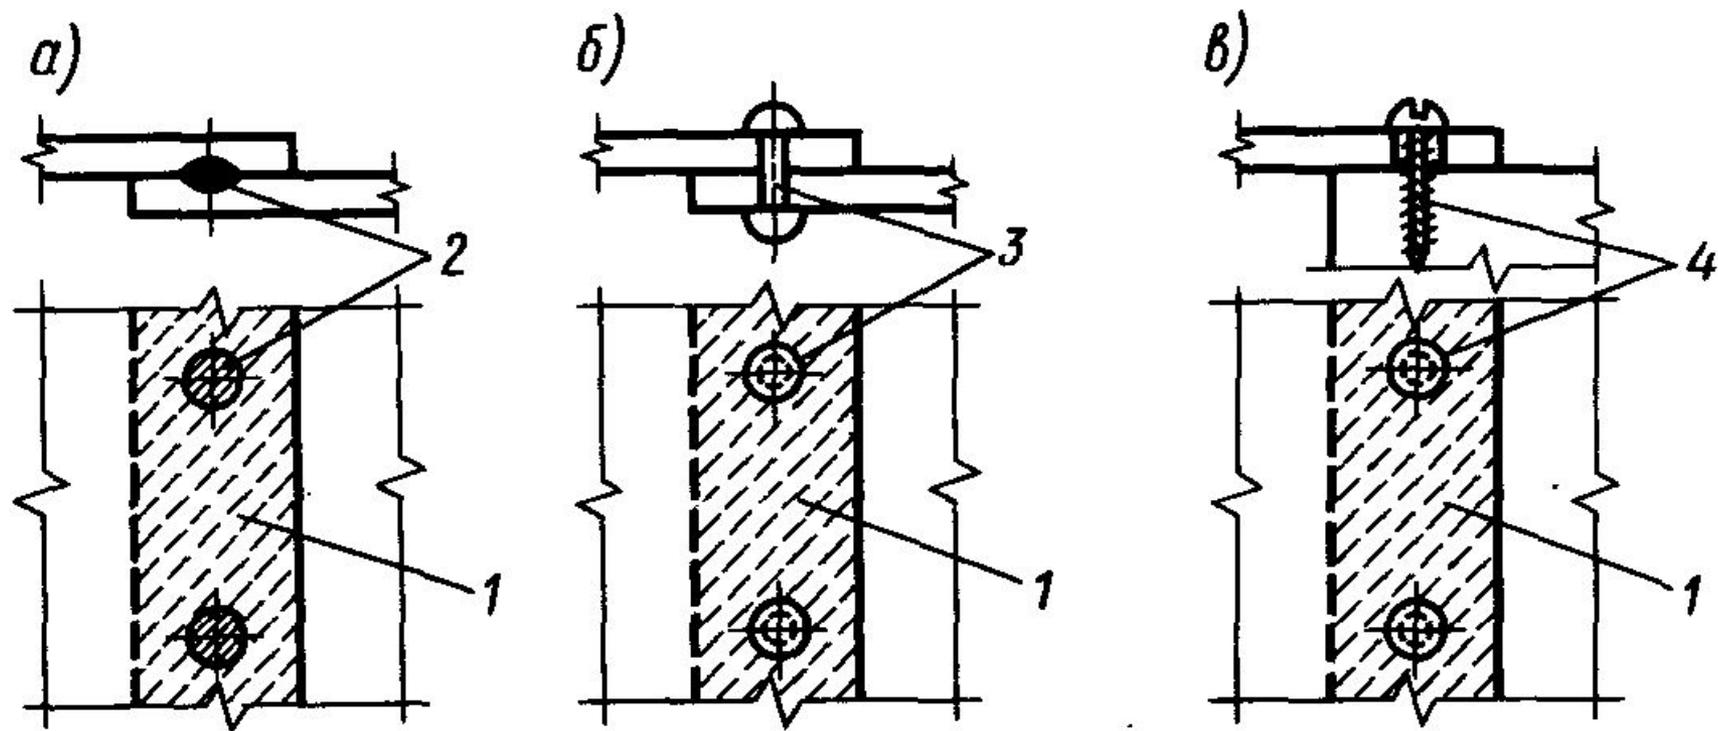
Клееметаллические соединения алюминиевых листов:
